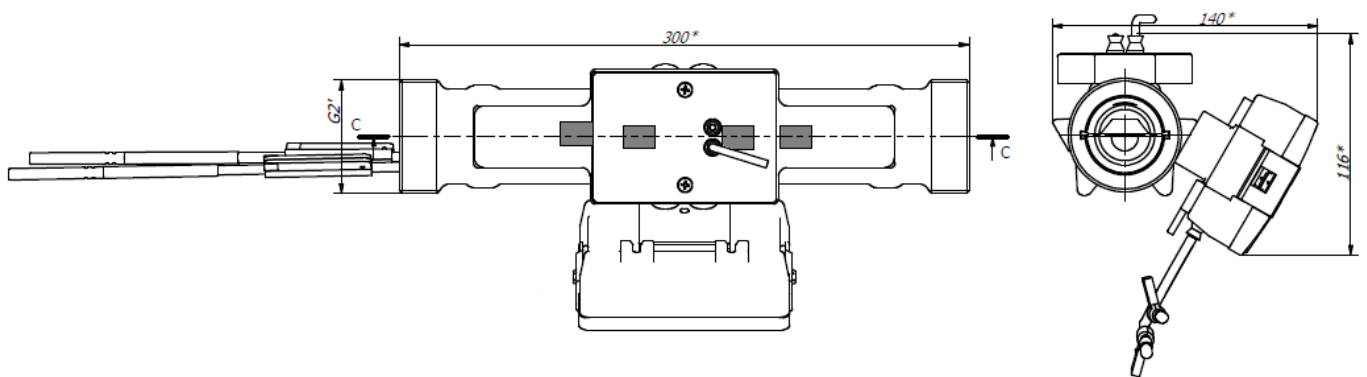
Присоединительный размер к трубопроводу Ду40, длина L=300 мм.
